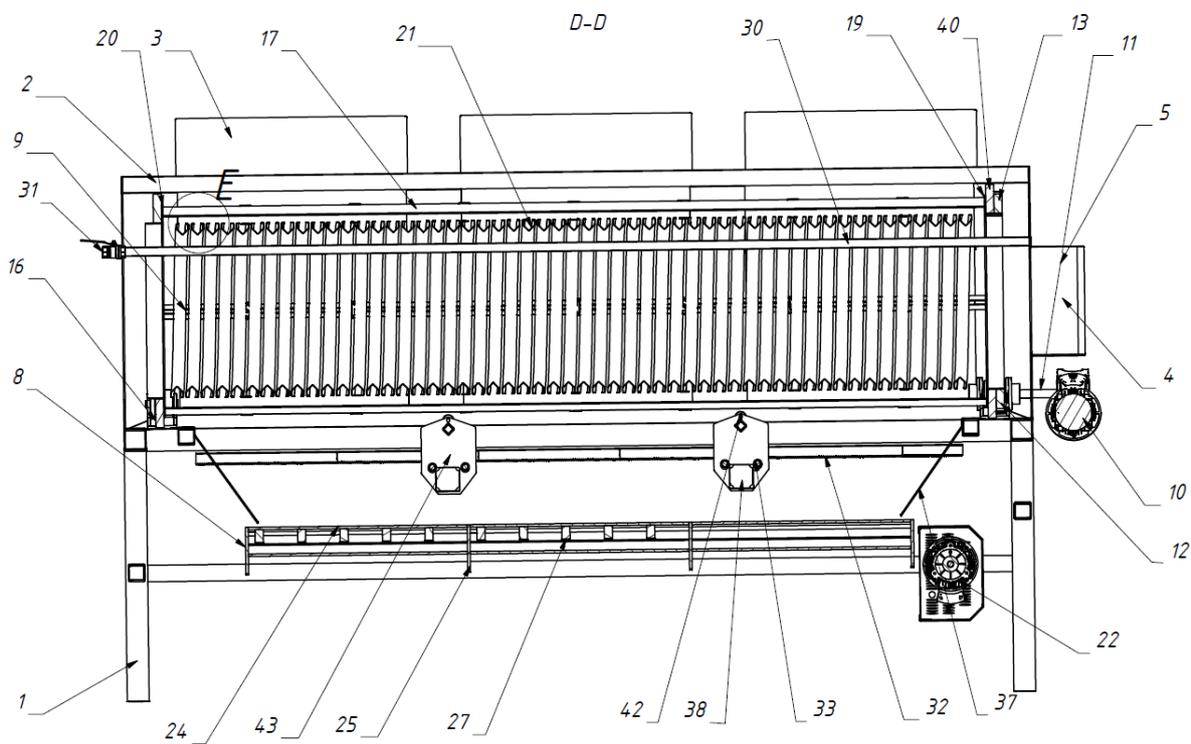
Схема машины для сортировки рыбы, вид справа
